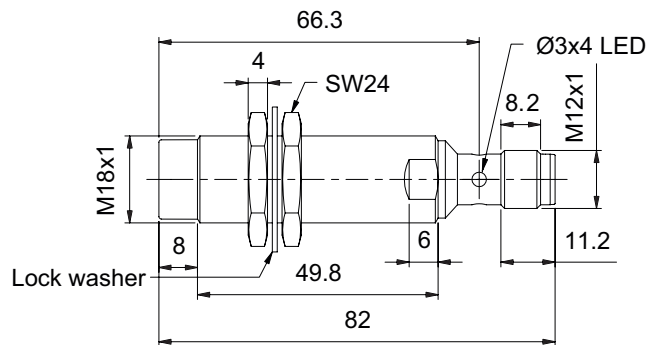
Uskærmet, ikke planmontage, M12-stik
